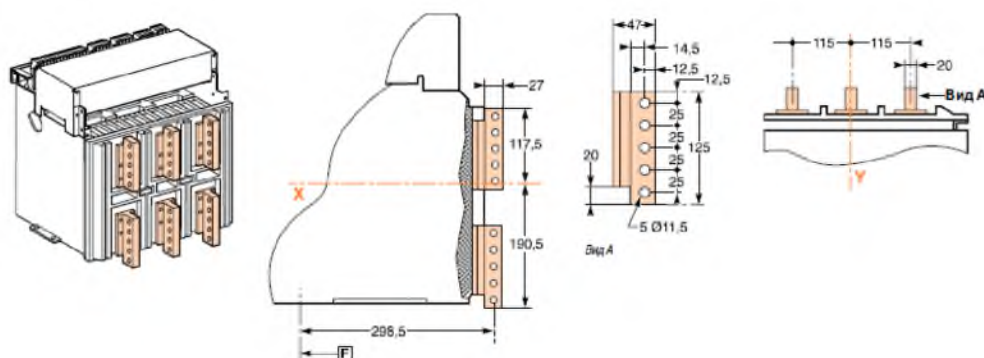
Горизонтальные и вертикальные выводы для заднего присоединения с присоединительными размерами для автоматического выключателя ВА–СЭЦ–АС40 выкатного исполнения
